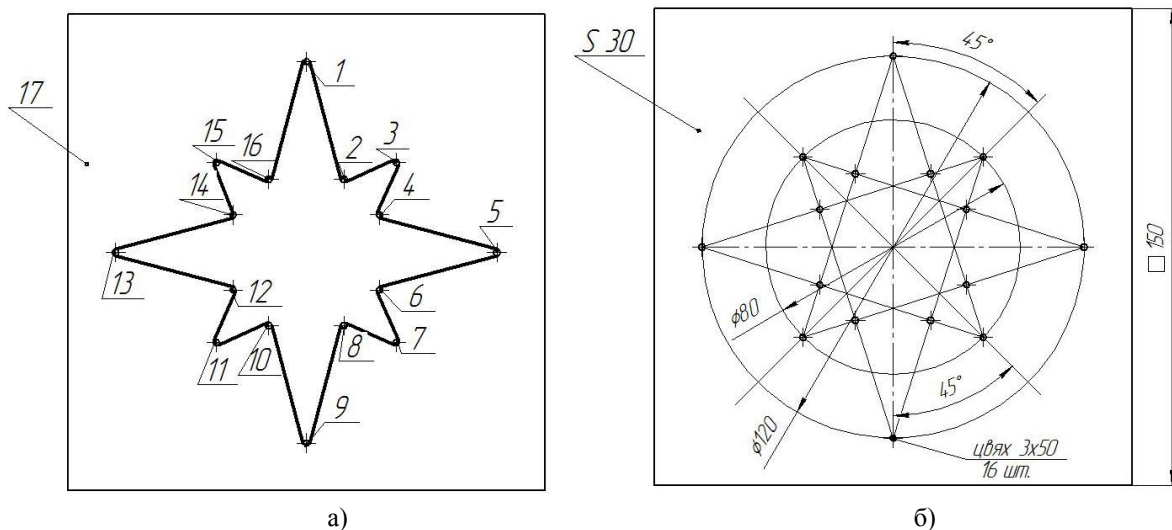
Копір для гнуття контуру форми для печива у вигляді зірки
